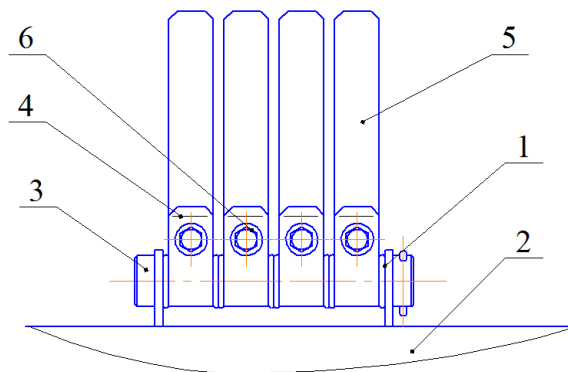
Били встановлені на очисника головок: 1 – вуха; 2 – труба; 3 – вісь; 4 – скоба; 5 – била; 6 – болтове з'єднання
